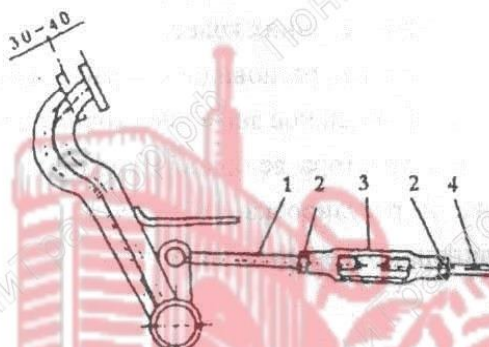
Регулировка свободного хода тормозной педали: 1,4-рычаги; 2-контргайки, 3- втулка
